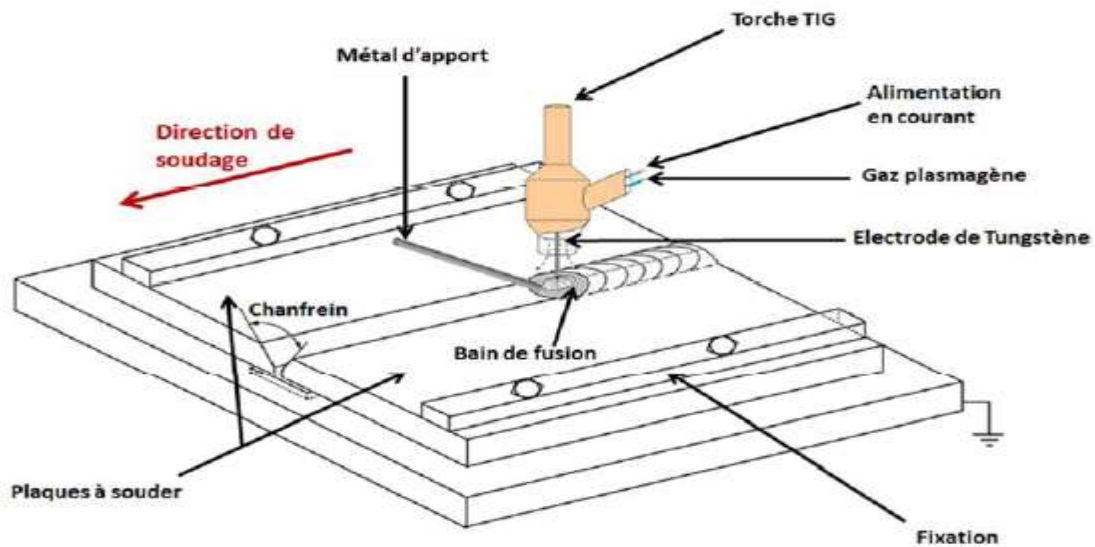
Schéma du procédé de soudage TIG [8].
